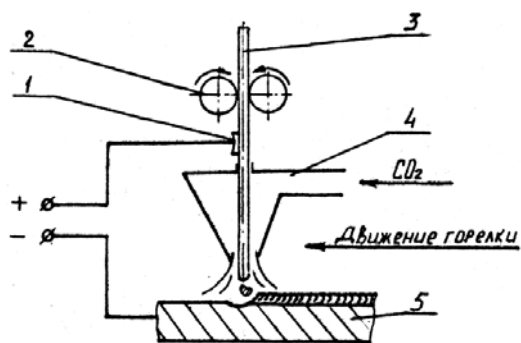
Схема сварки (наплавки) в углекислом газе:
